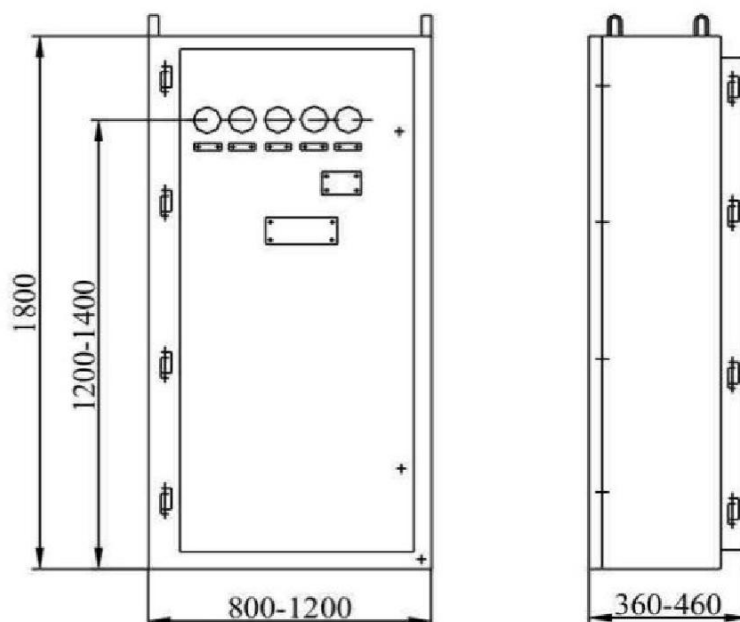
Габаритные размеры шкафов КРУ исполнения ШНВА
